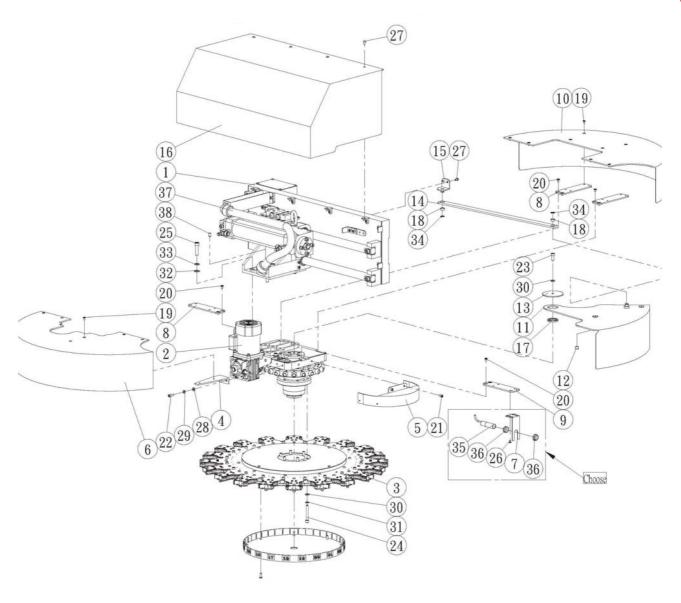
Werkzeugwechsler 1-4 -Tool changer 1-4
